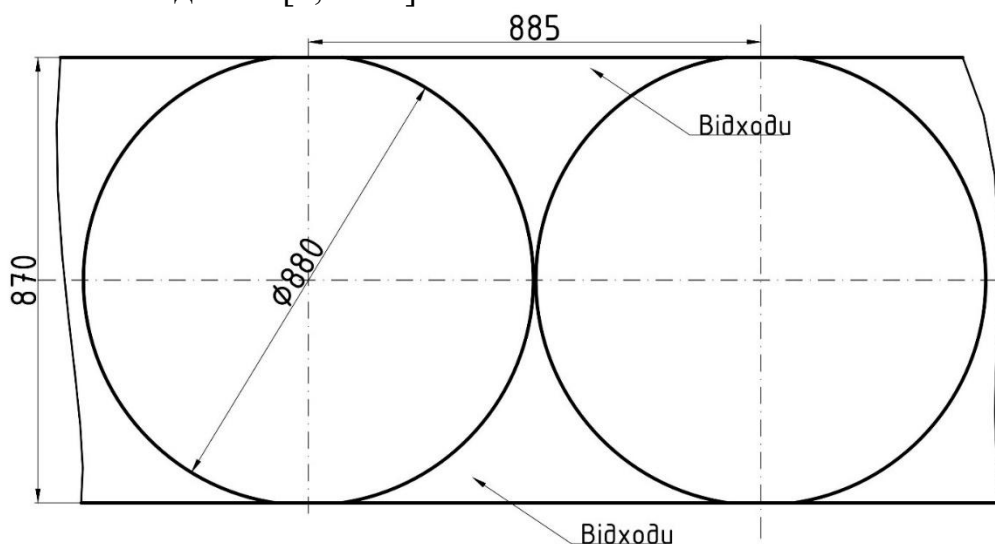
Схема розкрою заготовки Ø880 мм по базовому варіанту
